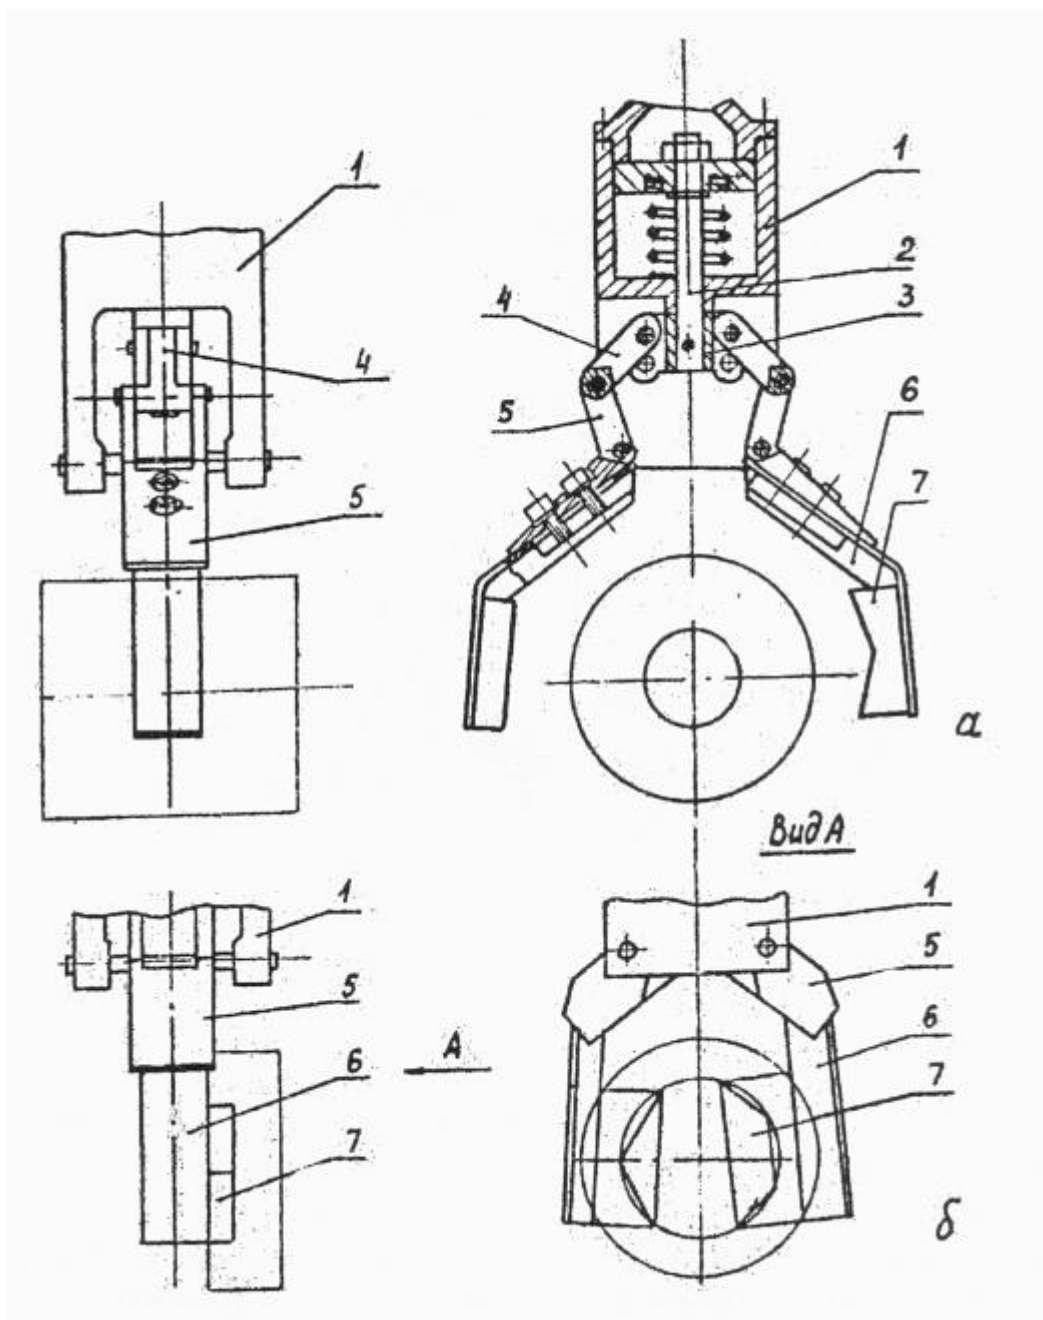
ЗУ для фланцев и колец с рычажным передаточным механизмом
